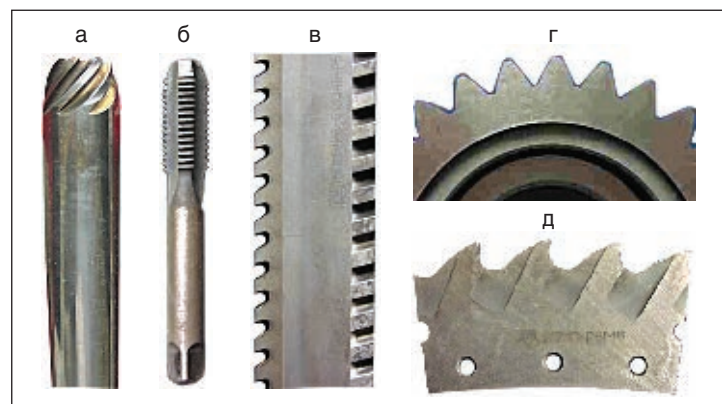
Инструмент после ИПО: а — концевая фреза; б — метчик; в — протяжка; г — зуборезная фреза; д — часть составной пилы
